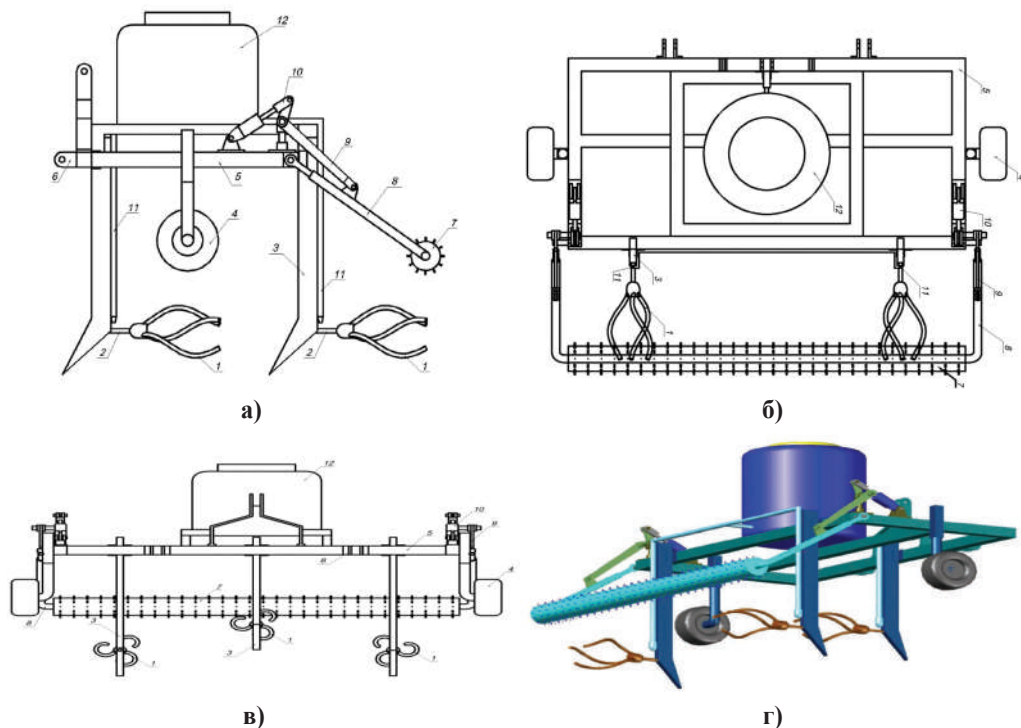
Схематический вид агрегата “Устройство глубокой обработки почвы”
